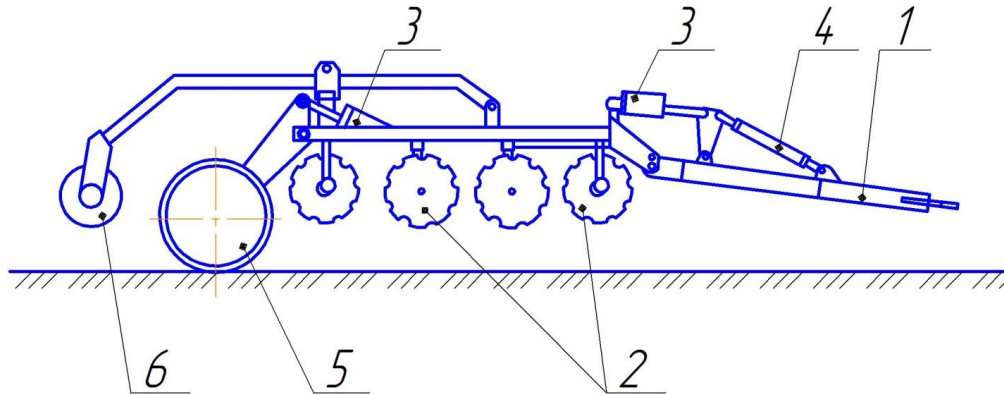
Схема борони [патент № 110895]: 1 – причіпне; 2 – робочий орган; 3 – гідроциліндр; 4 - тяга; 5 – транспортне колесо; 6 – коток.
